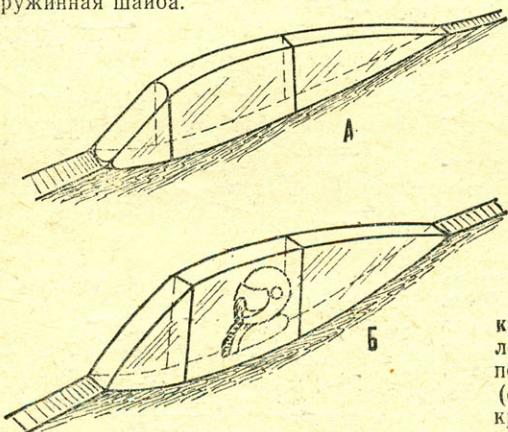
Фонарь пилотской кабинки: А — монолитный (оргстекло), Б — выkleенный из целлулоида.
